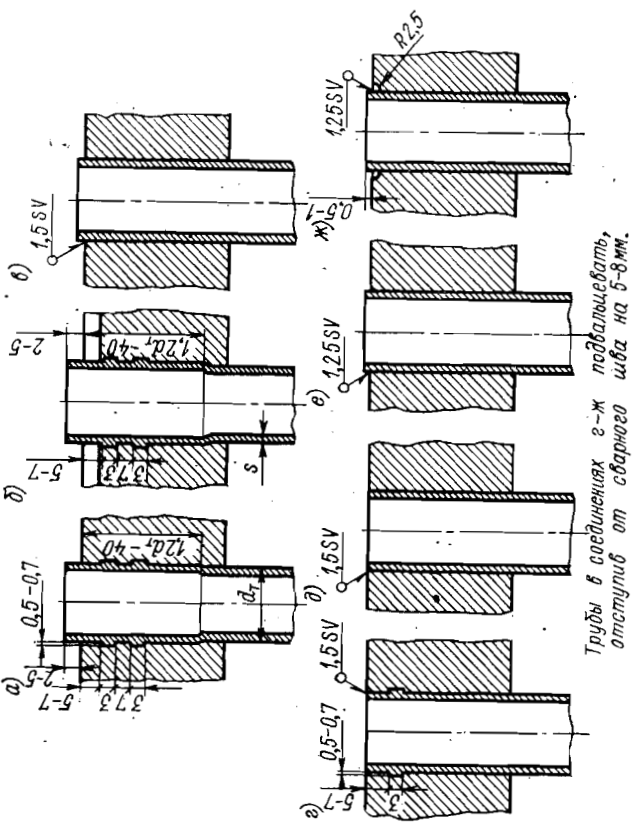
Конструкция соединений труб $d_T = 16 + 25$ мм в трубных решетках: а — с развальцовкой в двух канавках; б — то же в решетках из двухслойной стали; е — с обваркой; е-ж — с обваркой и подвальцовкой
